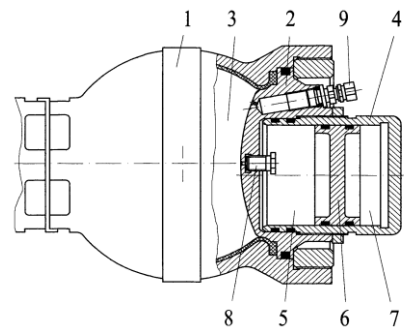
Рессора с гидропневматическим цилиндром компенсации: 1 – корпус пневматического баллона рессоры; 2 – крышка; 3 – пневматическая полость рессоры; 4 – гидропневматический цилиндр компенсации; 5 – пневматическая полость цилиндра компенсации; 6 – поршень; 7 – гидравлическая полость цилиндра компенсации; 8 – дроссель; 9 – зарядный клапан
